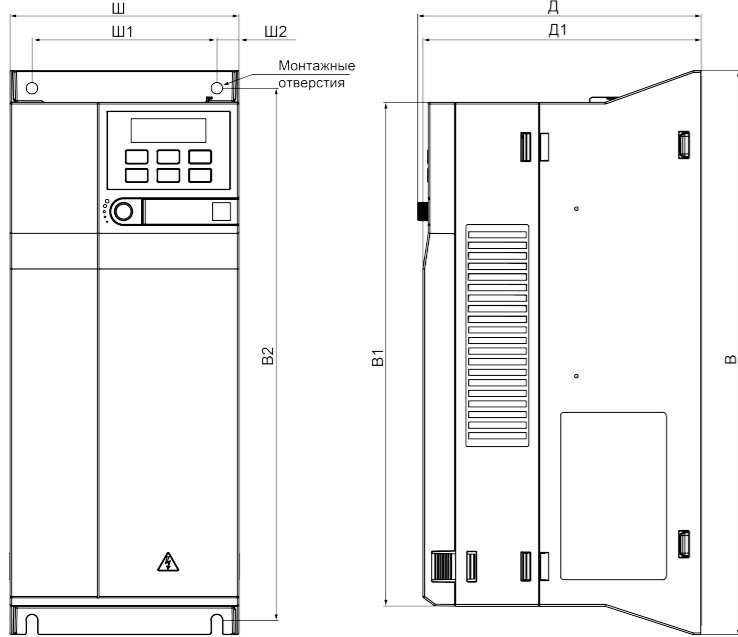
Габаритные и присоединительные размеры прибора типоразмеры 3 и 4
